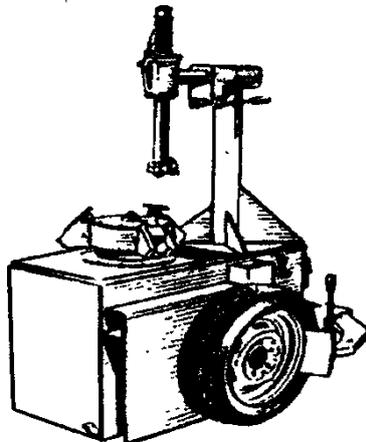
Стенд для демонтажа и монтажа колес легковых автомобилей
